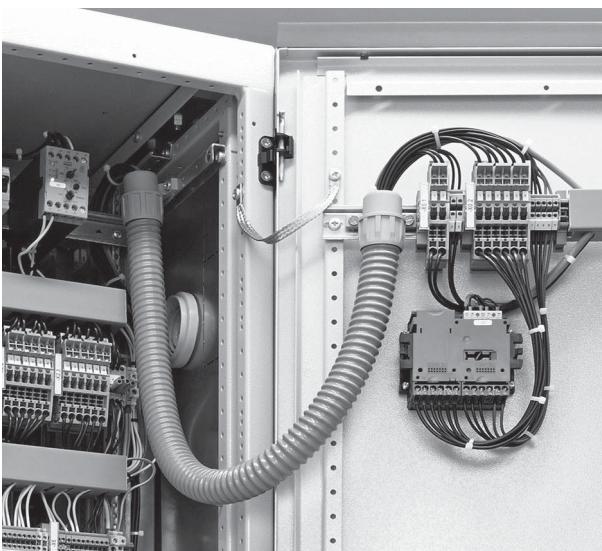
Tür mittels Erdungsband mit dem Schrankgerüst verbunden
